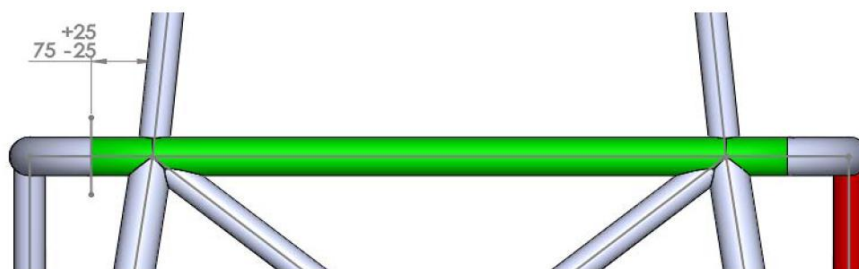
Vista en planta del detall de l'arc principal, cotes en mm.
